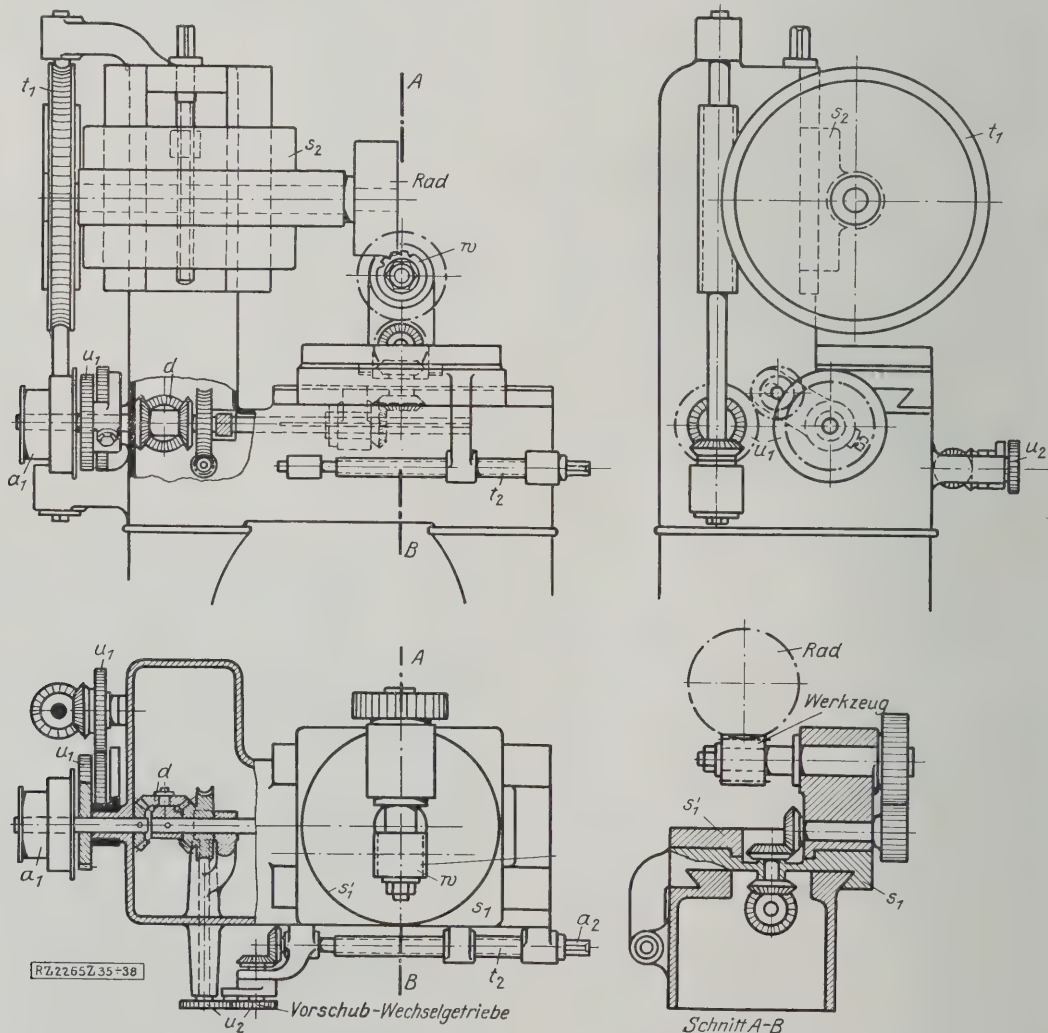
bis 38. Maschine von Pfauter zum Fräsen von Schraubenrädern mittels Schneckenfräasers (nach der Patentschrift 112 082 vom 27. Juli 1900)
